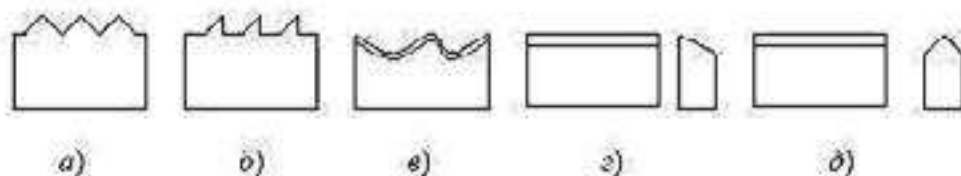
Формы режущей поверхности: а – острая; б – зубчатая; в – дугообразная зубчатая; г – гладкая односторонней заточки; д – гладкая двусторонней заточки
